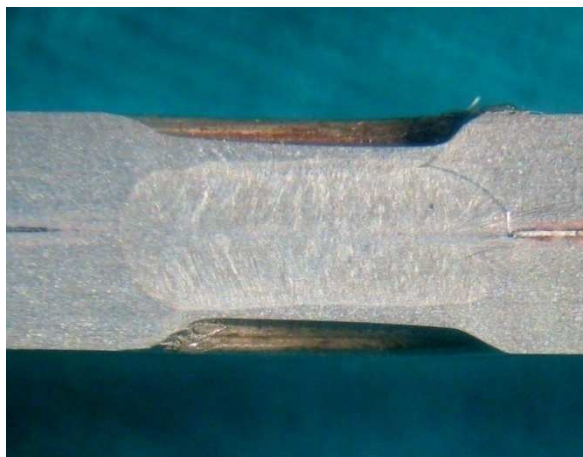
22. Macrografía del punto de soldadura en la probeta de 2.0 mm (10x)
